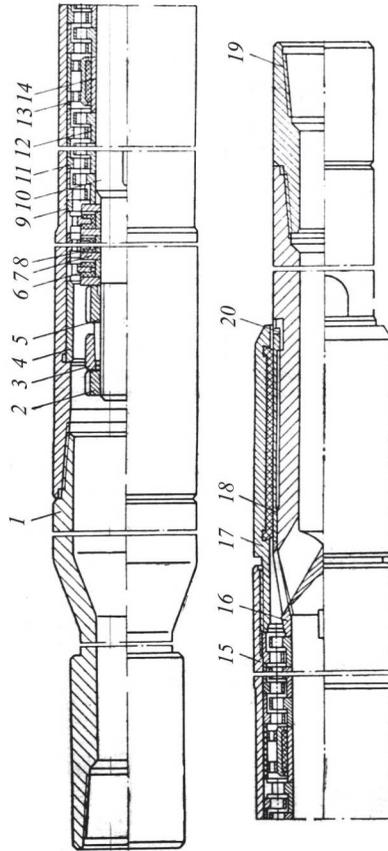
Турбобур: 1 – переводник; 2 – контргайка; 3 – колпак; 4 – упорная втулка; 5 – роторная гайка; 6 – подпятники; 7 – диски пяты; 8 – кольца пяты; 9 – регулировочное кольцо; 10 – вал; 11 – статор; 12 – ротор; 13 – средняя опора; 14 – втулка промежуточной опоры; 15 – корпус; 16 – упор; 17 – ниппель; 18 – втулка нижней опоры; 19 – переводник; 20 – шпонка
